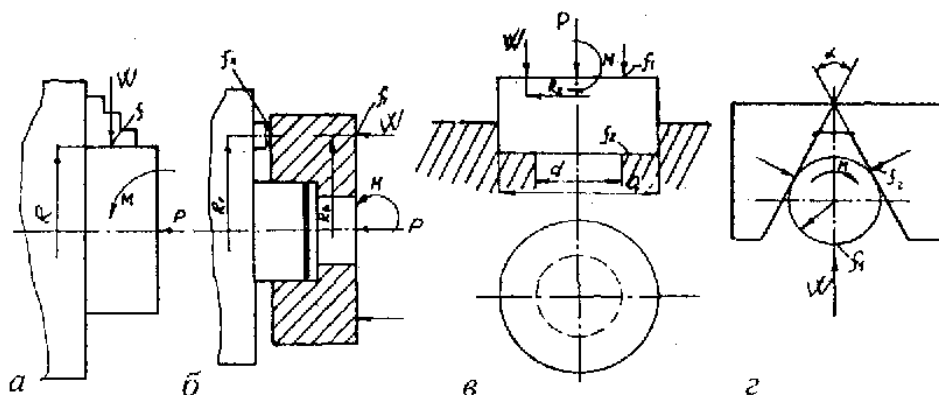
Розрахункові схеми для визначення затискних зусиль заготовки від прокручування
